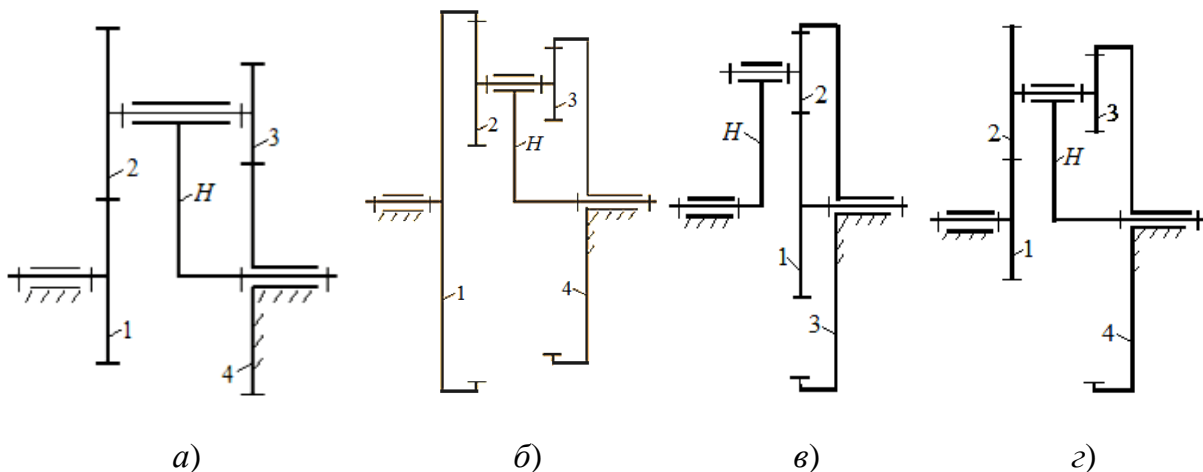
Кинематические схемы планетарных механизмов: а – механизм с двумя внешними зацеплениями (редуктор Давида); б – механизм со сдвоенными сателлитами и двумя внутренними зацеплениями; в – механизм Джеймса; г – механизм со сдвоенными сателлитами
